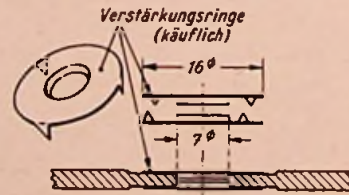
Ausführung einer Ringverstärkung. Die Ringe sind unter Erwärmen fest zusammenzudrücken, so daß sie nicht über die Schallplattenoberfläche hinausragen
